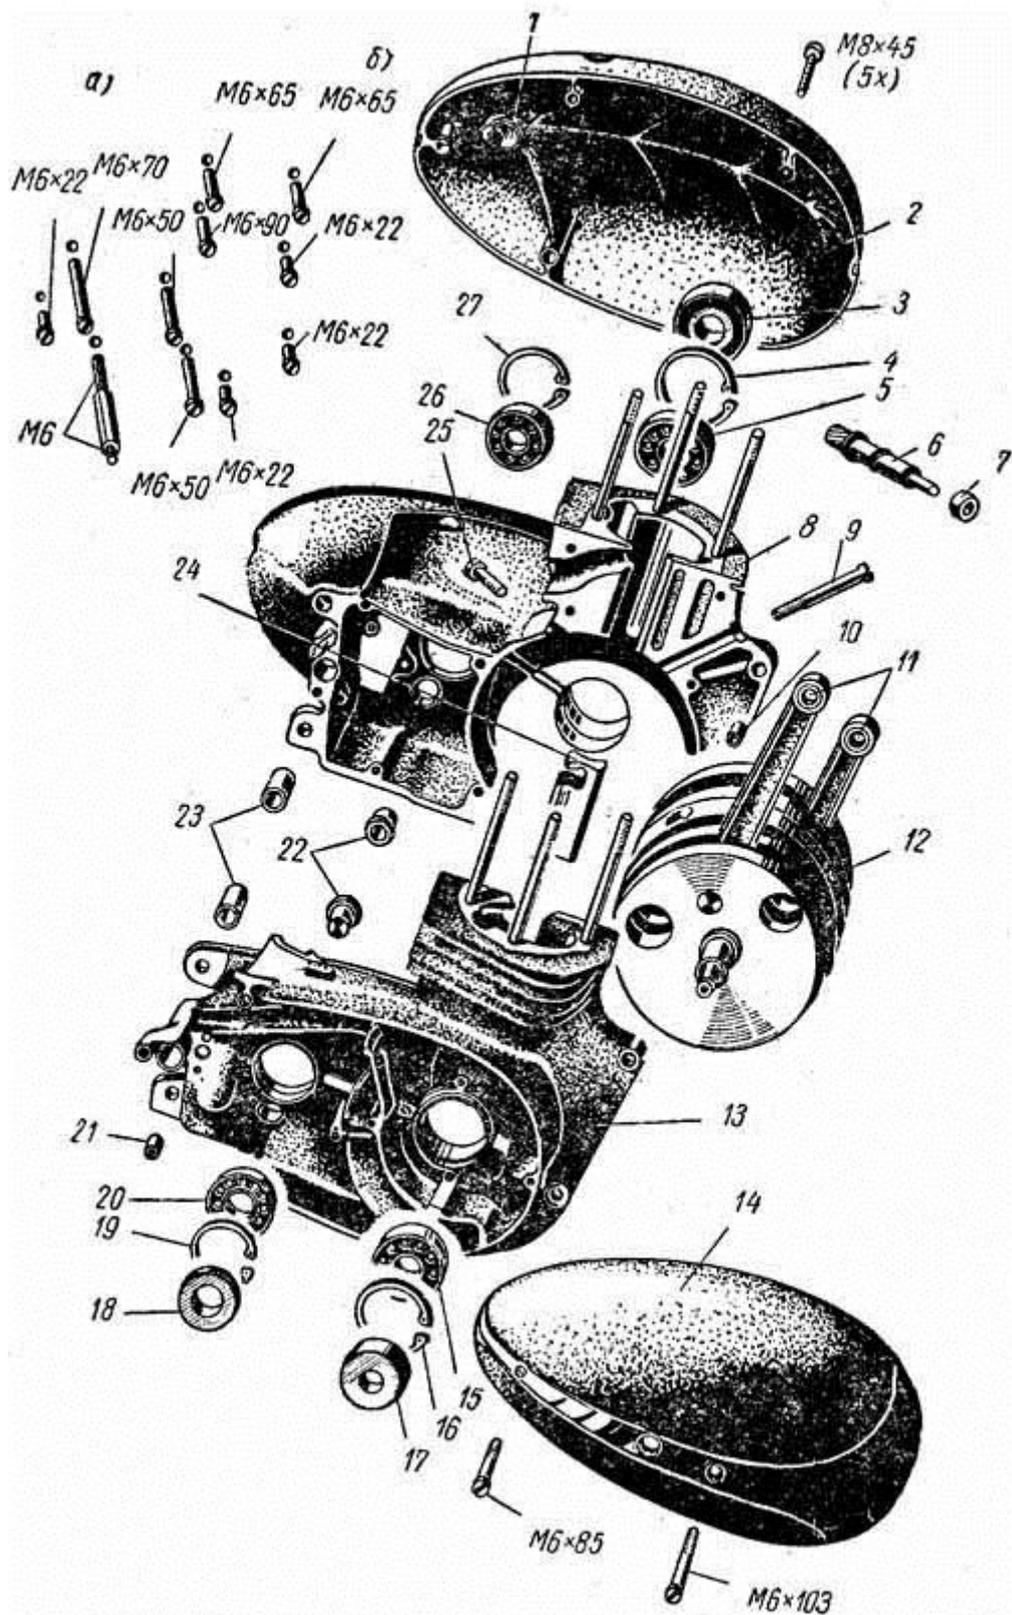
Схема расположения винтов, скрепляющих картер (а), и детали силового агрегата Ява-350 (б):
